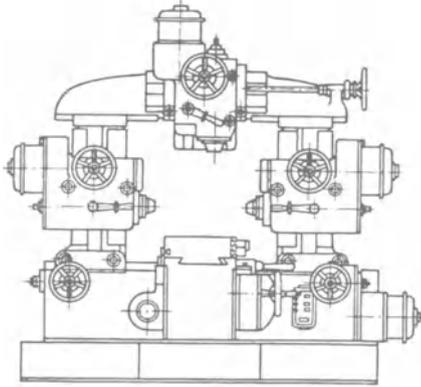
Mehrmotorenantrieb einer Planfräsmaschine.
